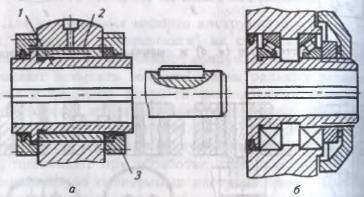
Направляющие втулки для борштанг с подшипником скольжения (a) и качения (b)
